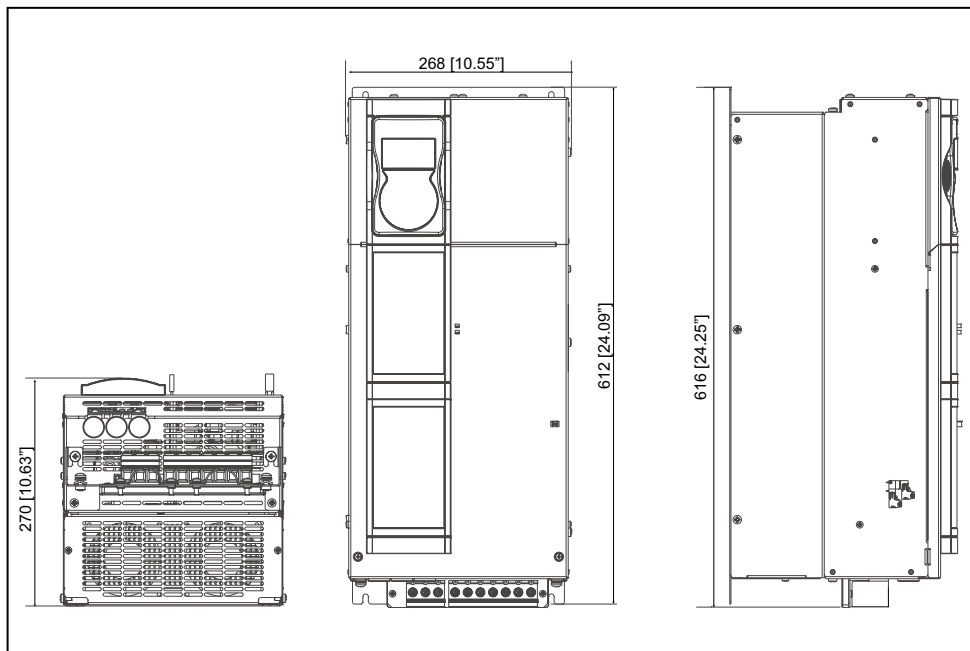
Размеры для типоразмера 4 (ADV200-...-4-DC)
